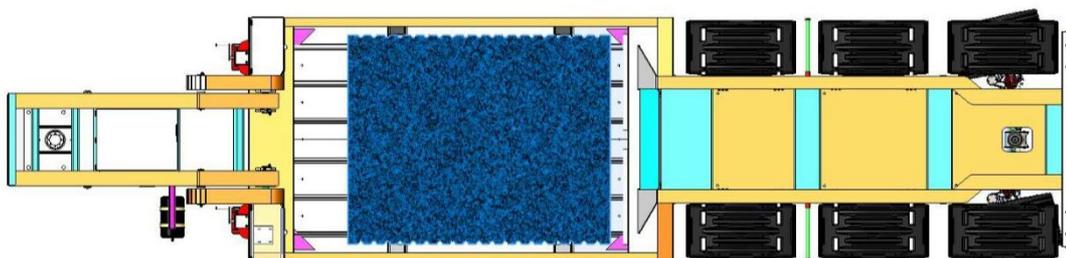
Vista superior do equipamento proposto carregado em formato 3D. Fonte: Próprio Autor (2018)
